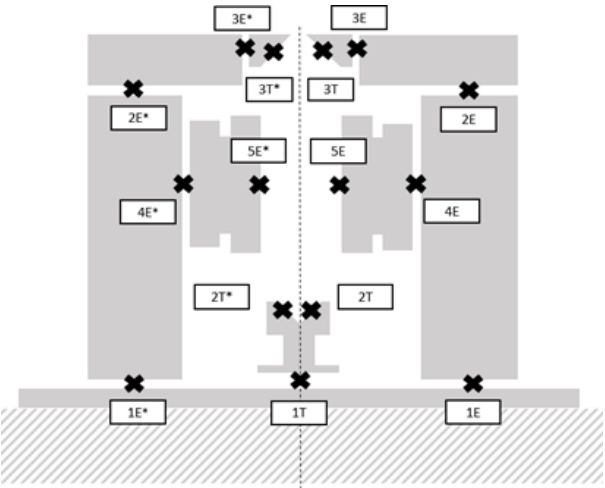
Vista esquemática de los parámetros de tolerancia de montaje.
